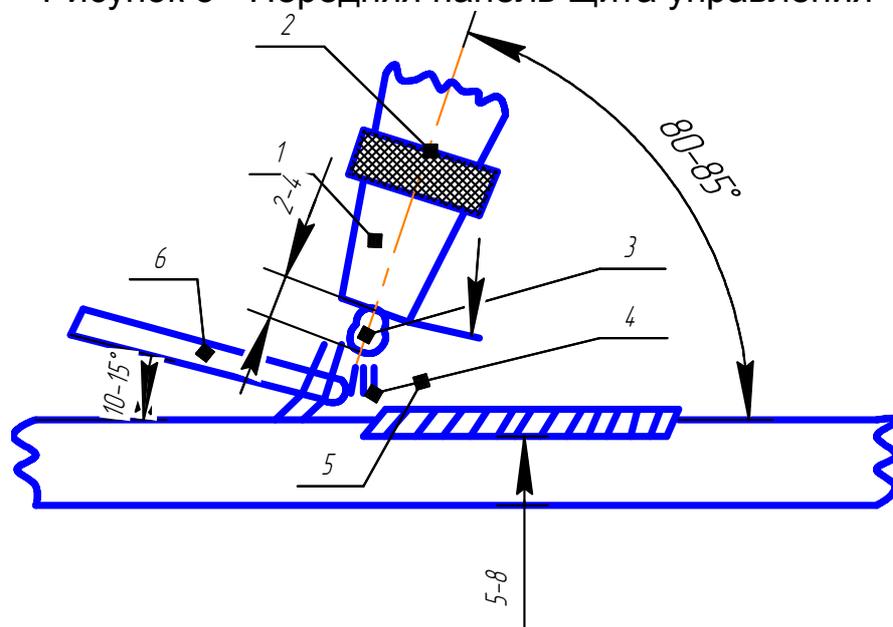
Принципиальная схема установки для аргоно-дуговой сварки и наплавки
